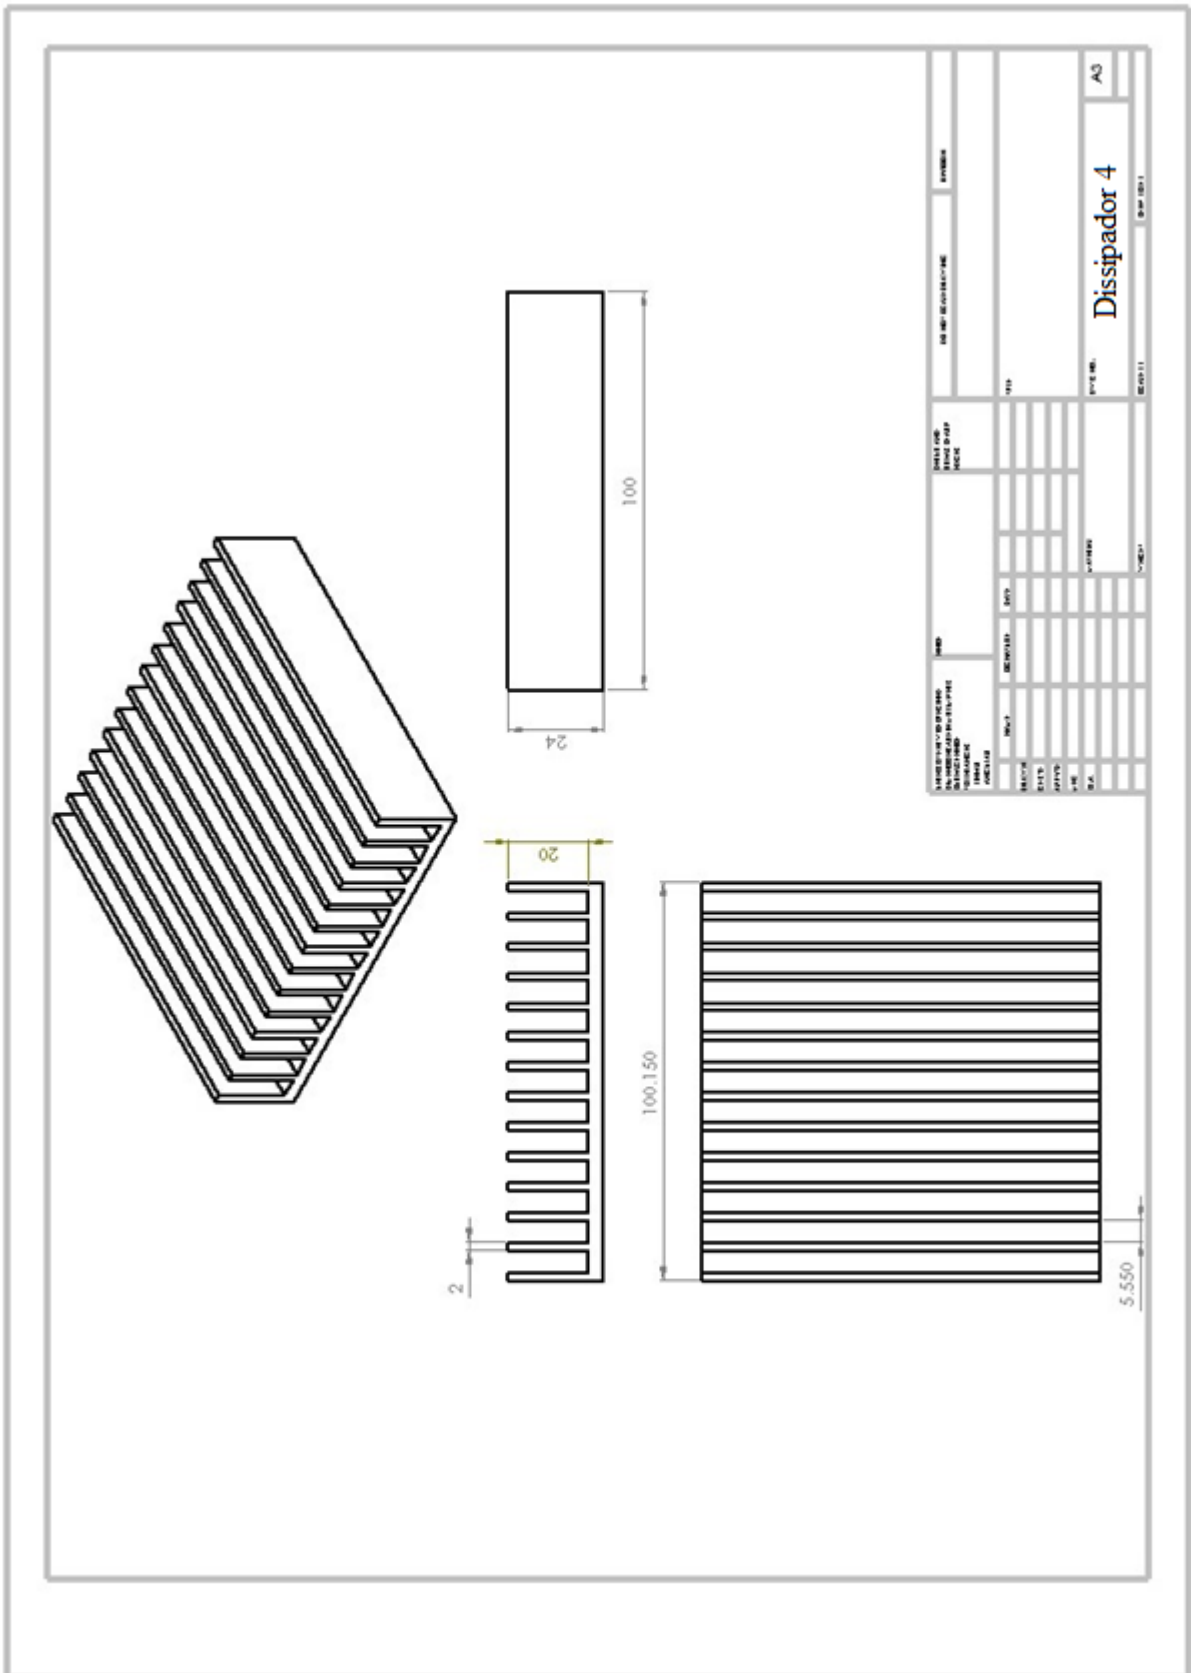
Desenho técnico utilizado para confecção do Dissipador 4.
